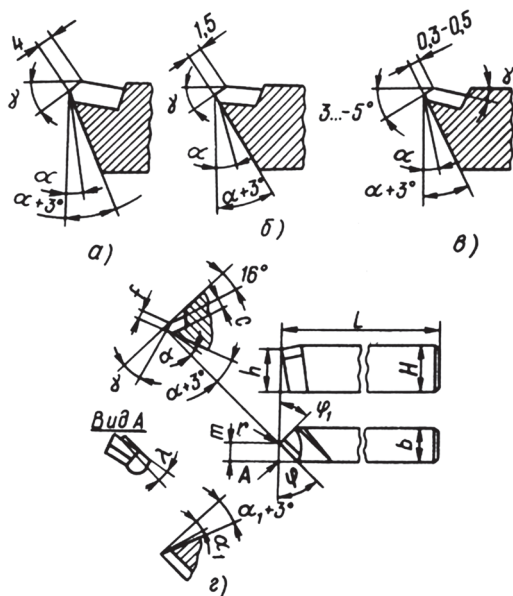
Геометрия и форма заточки резцов с пластинками твердых сплавов:
